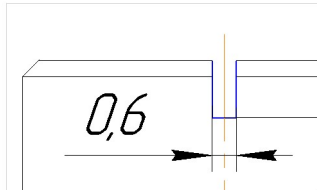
Ескіз поверхні для обробки фрезою
